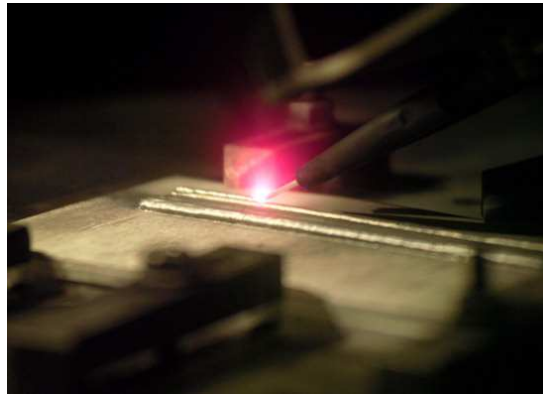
141313 Soldadura con rayo de electrones
